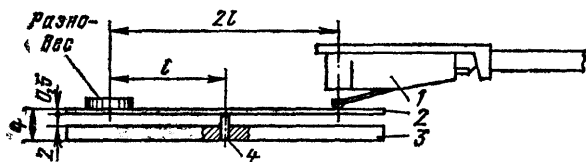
Приспособление для тарировки прижимной силы звукоснимателя.
